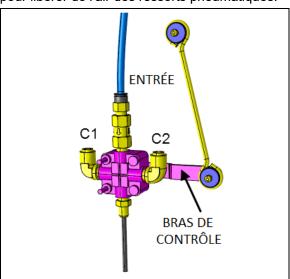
SOUPAPE DE COMMANDE DE HAUTEUR
